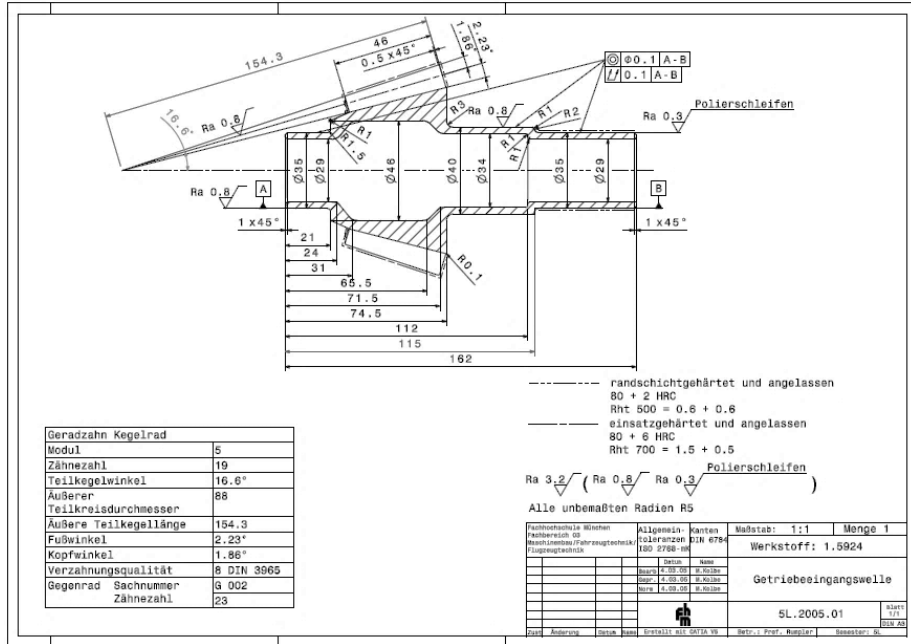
Aus Einzelteilen und Baugruppen können Sie technische Zeichnungen ableiten.
